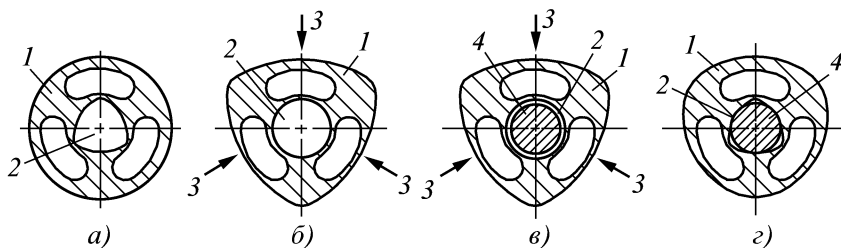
Этапы закрепления инструмента в патроне TRIBOS-R
